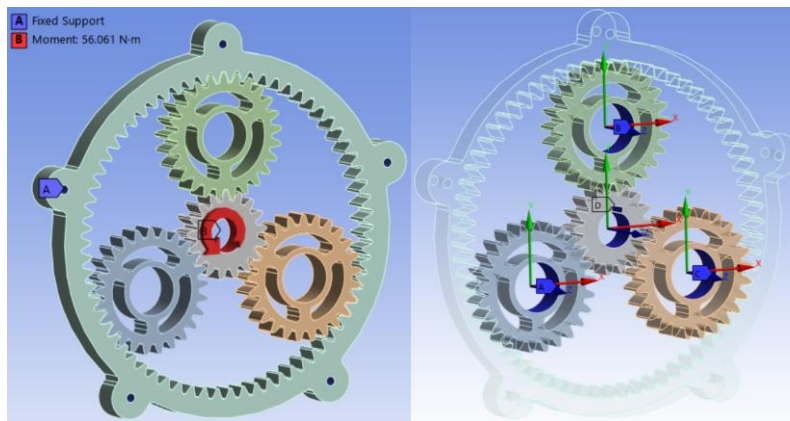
Condiciones de frontera del tren de engranajes planetarios optimizado.
